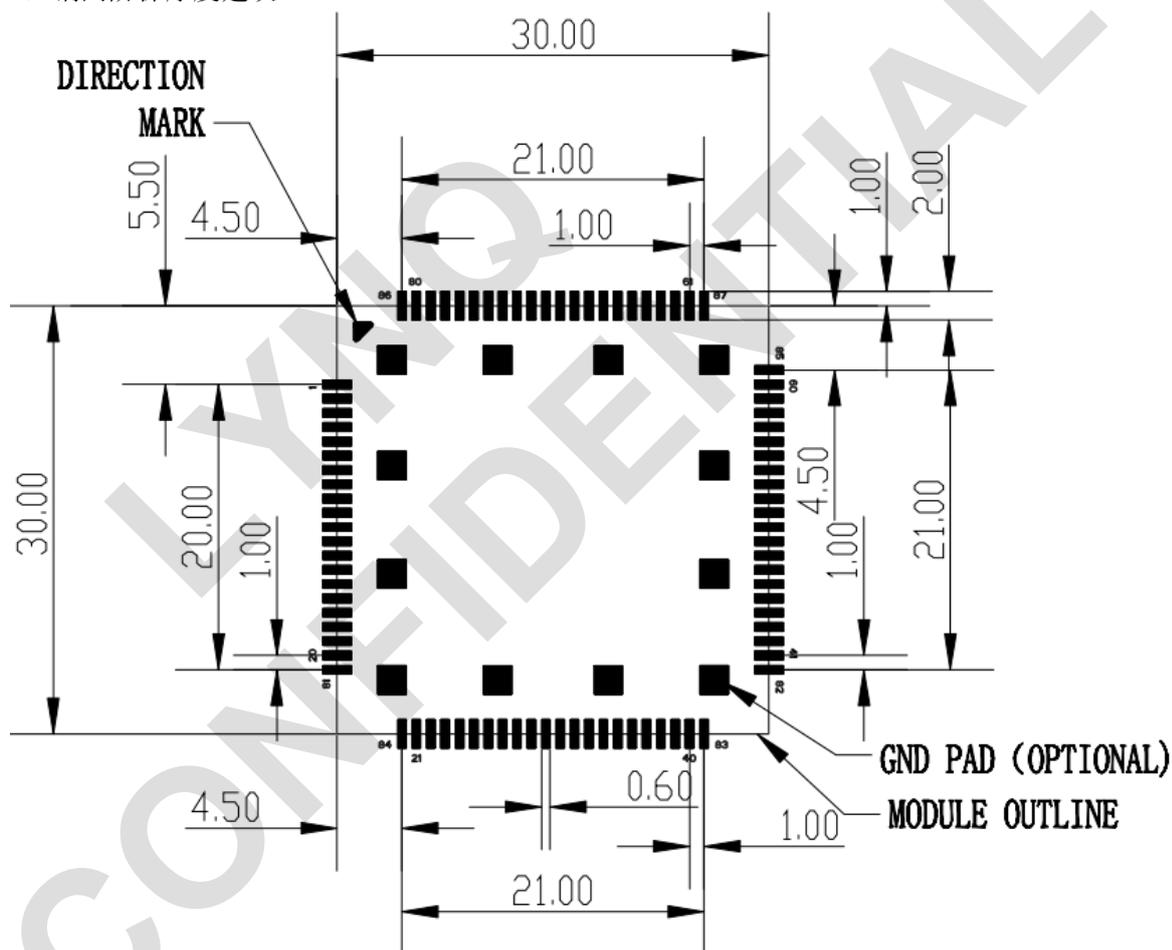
推荐焊盘钢网Top view (detail A)
